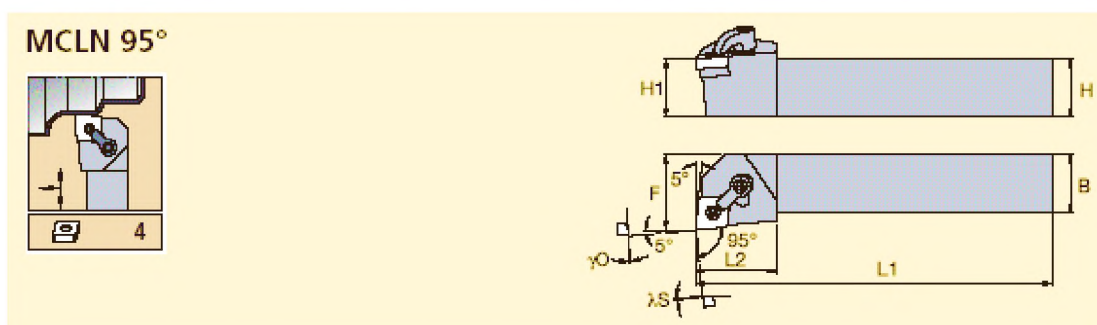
Державка різця – MCLNR3232P19.
